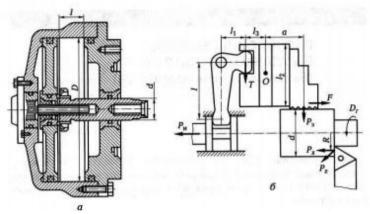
Схема пневмоцилиндра (а) и кулачкового патрона (б)
